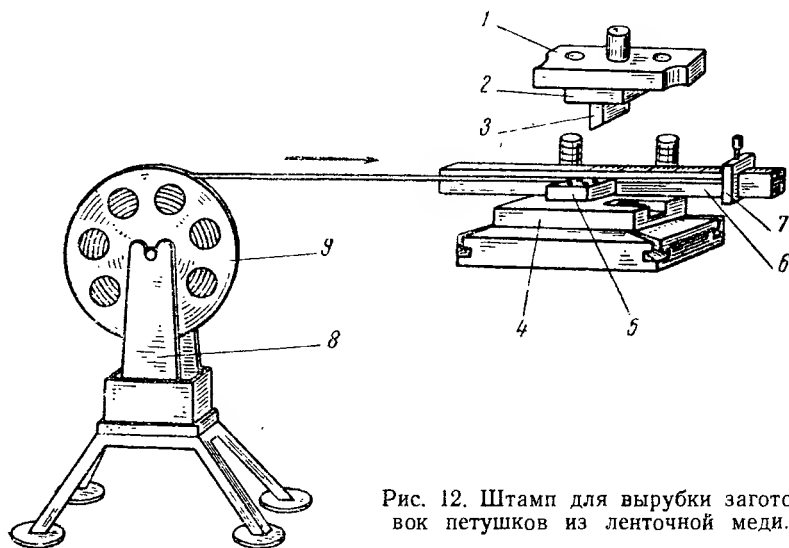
Штамп для вырубки заготовок петушков из ленточной меди.
